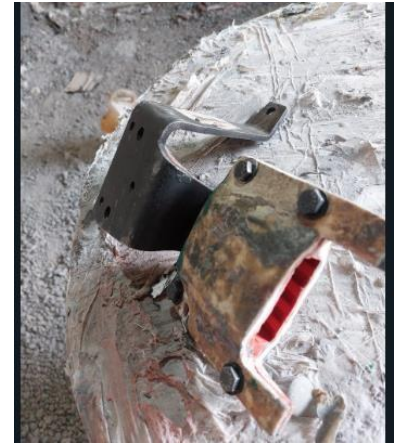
Pieza atornillada con el molde 2, para ser rellenada con la resina.
